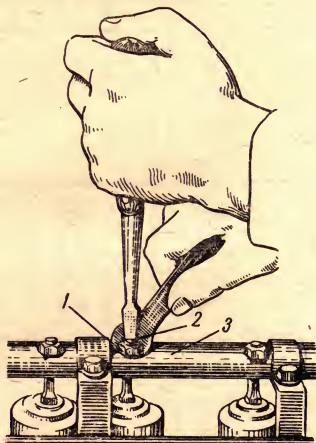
Регулировка декомпрессионного механизма двигателей Д-50Л, Д-65М и Д-65Н:
